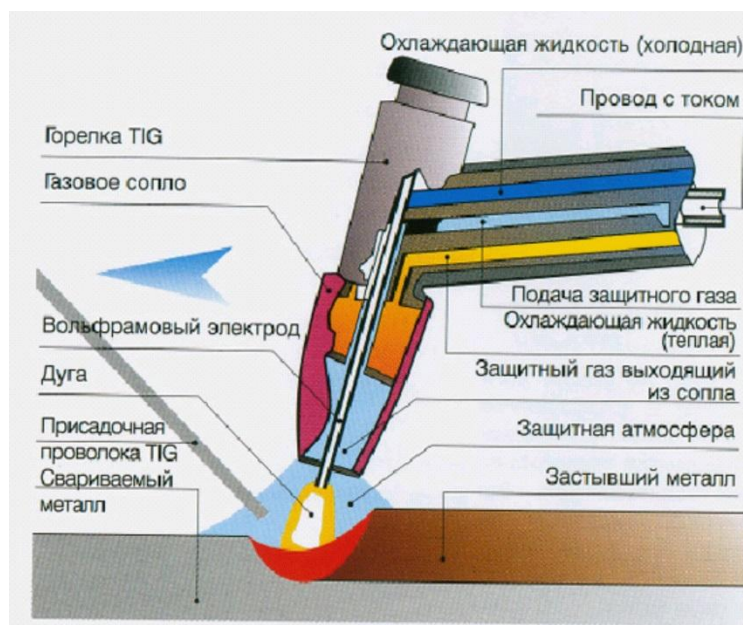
Схема сварки неплавящимся электродом в инертном газе
